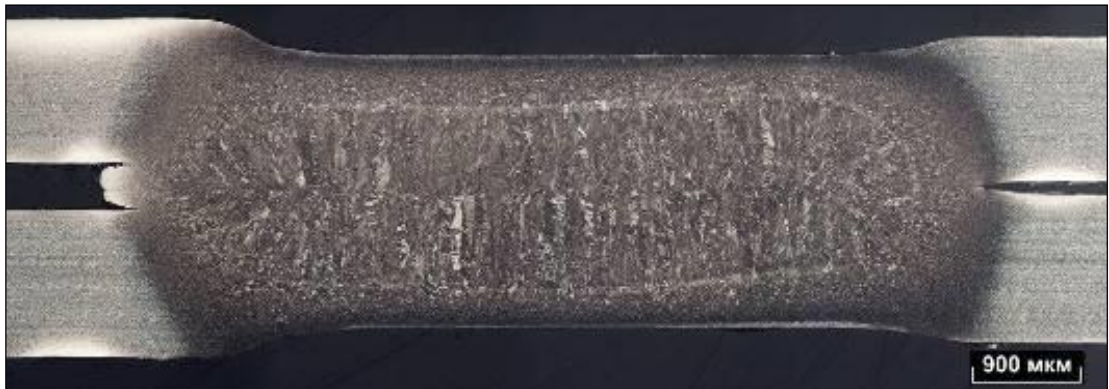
Макроструктура сварной точки 4.1.1
